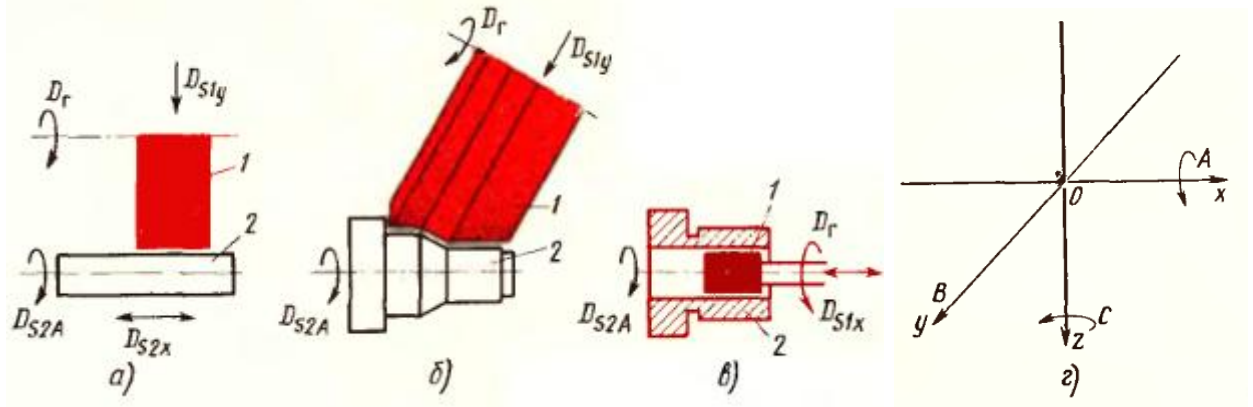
Элементы движений круга (1) и заготовки (2) при шлифовании:
